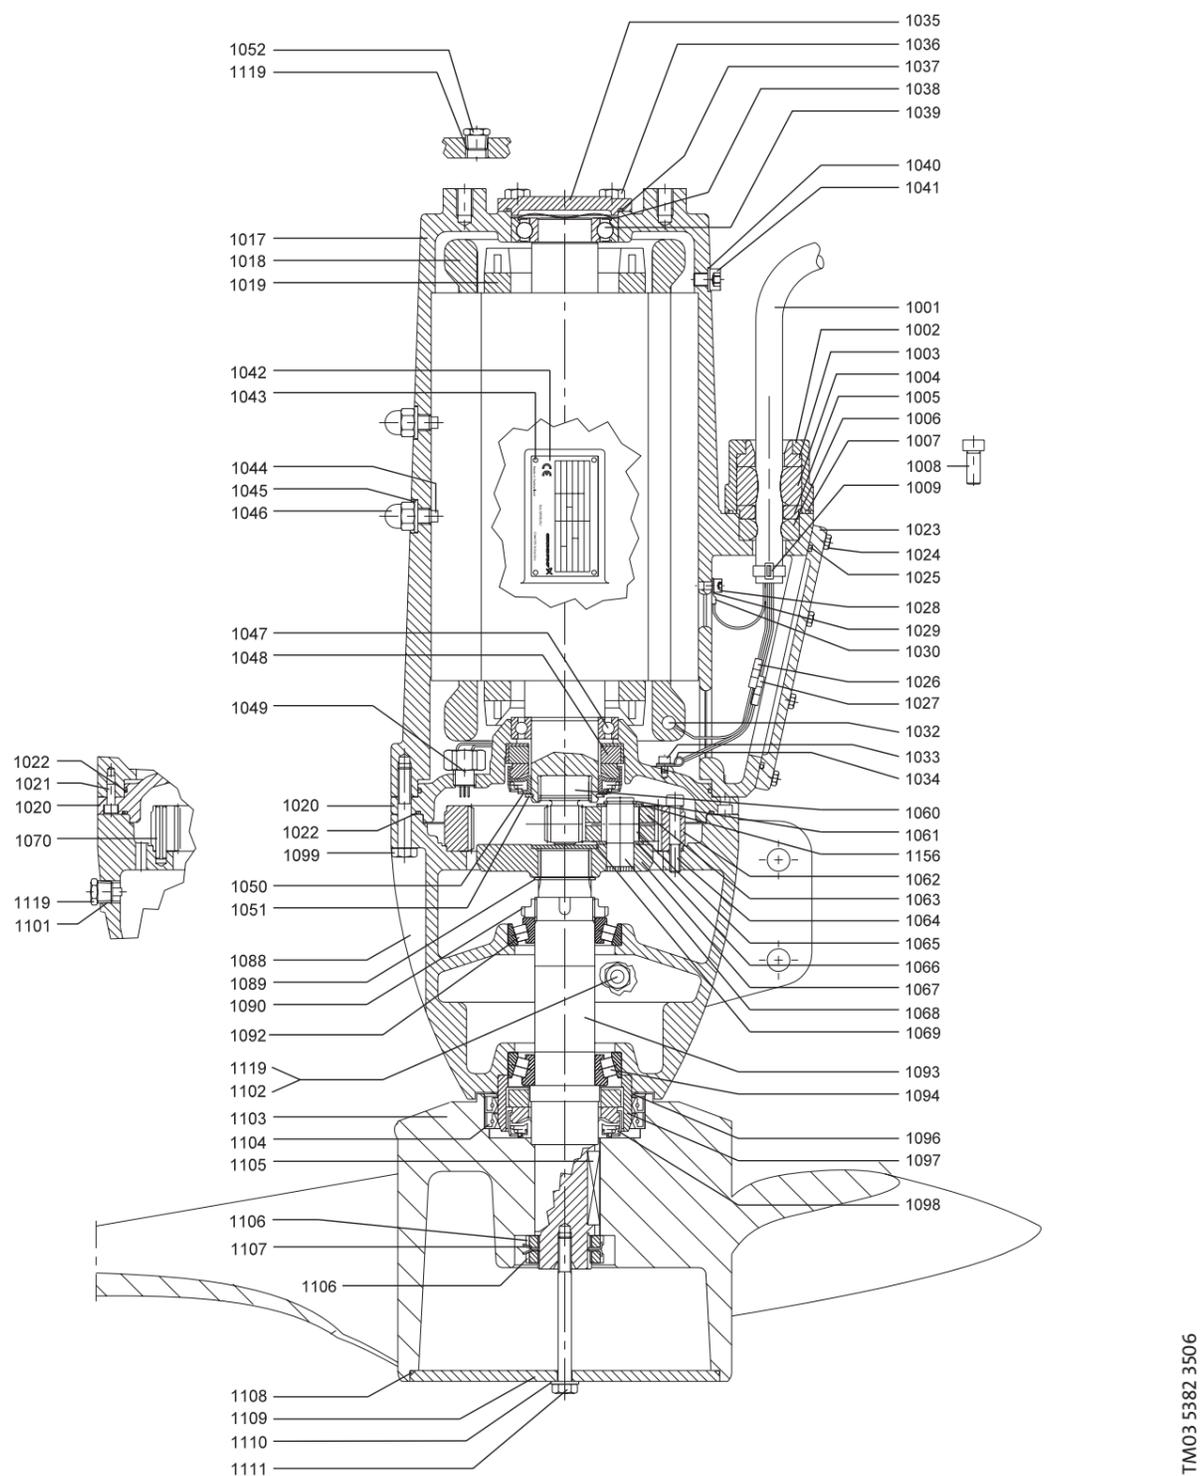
Чертеж в разрезе, SRP.70.80.xxx, SRP.100.80.xxx и SRP.130.80.xxx
